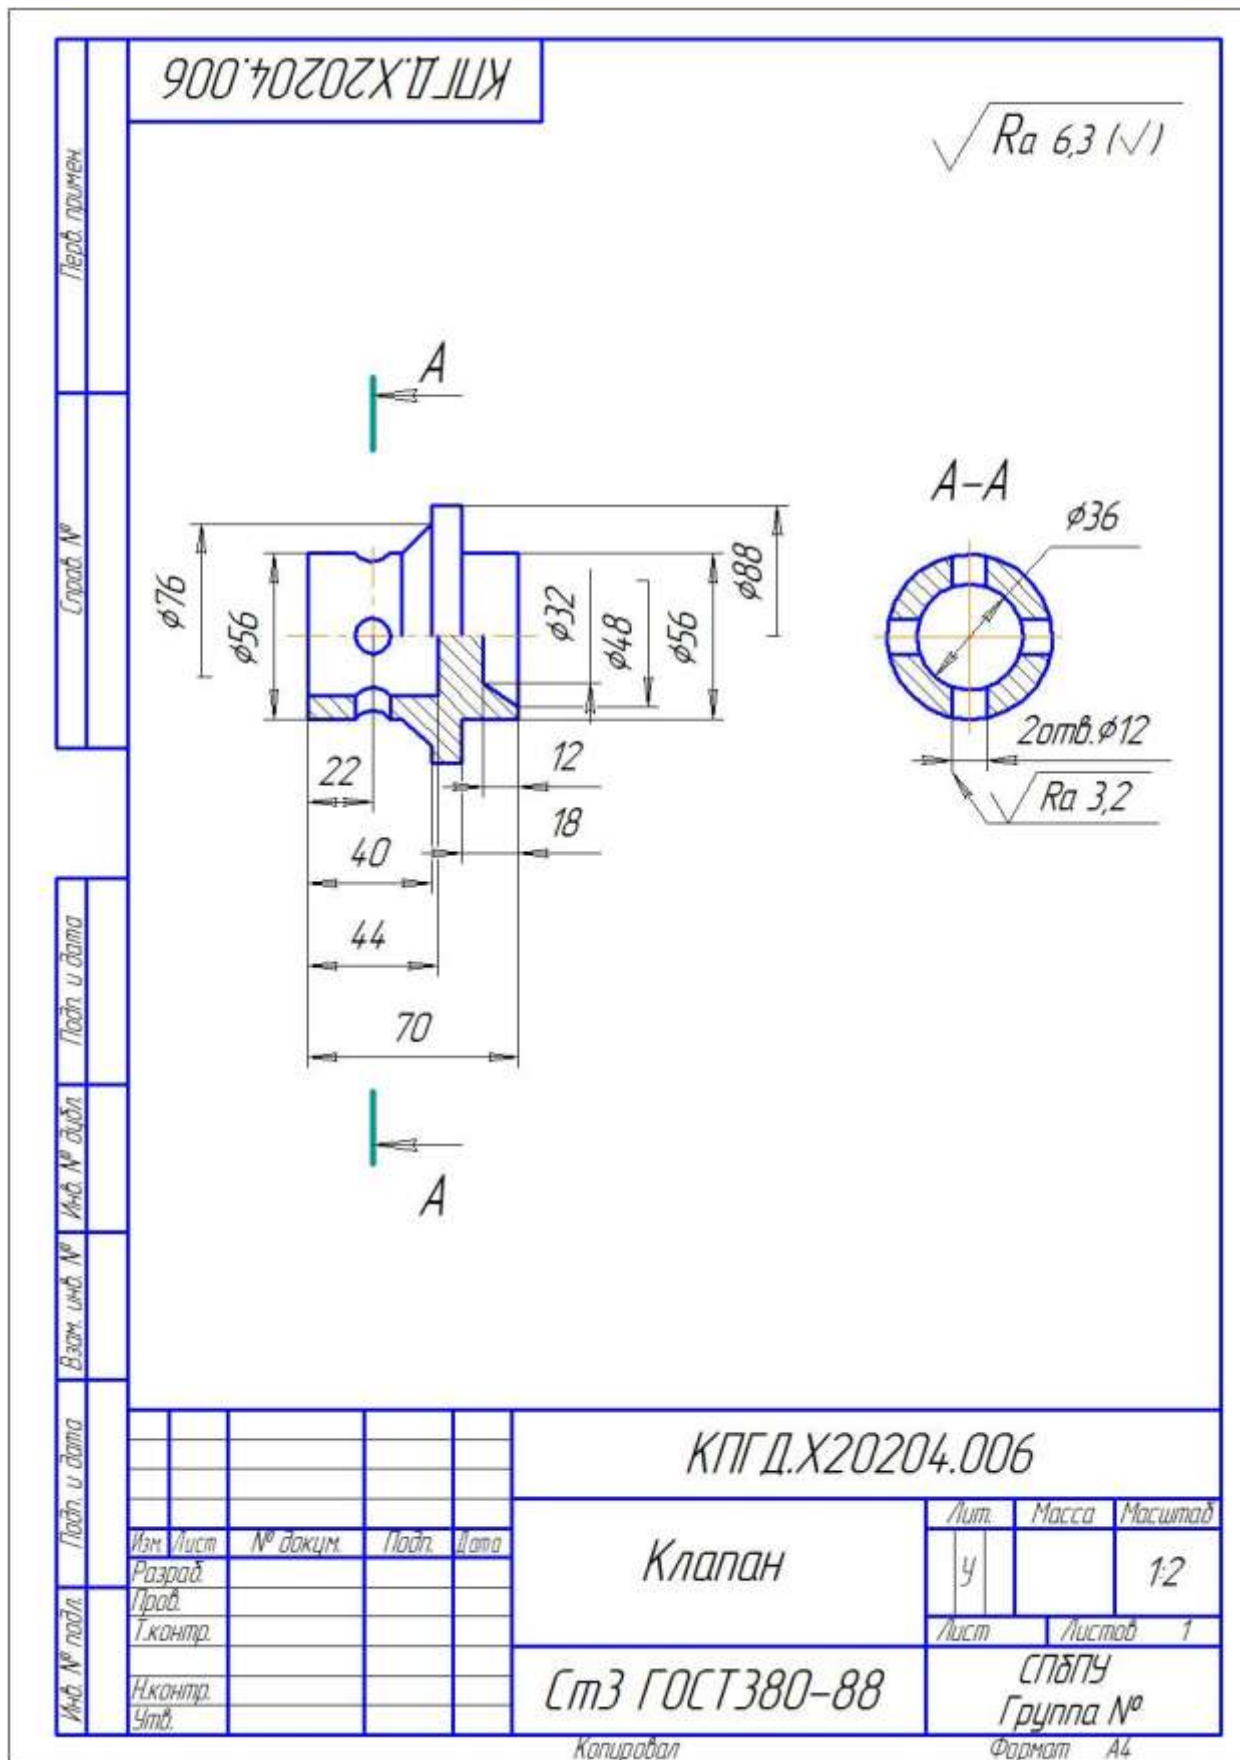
Пример выполнения рабочего чертежа деталь №6 - Клапан
